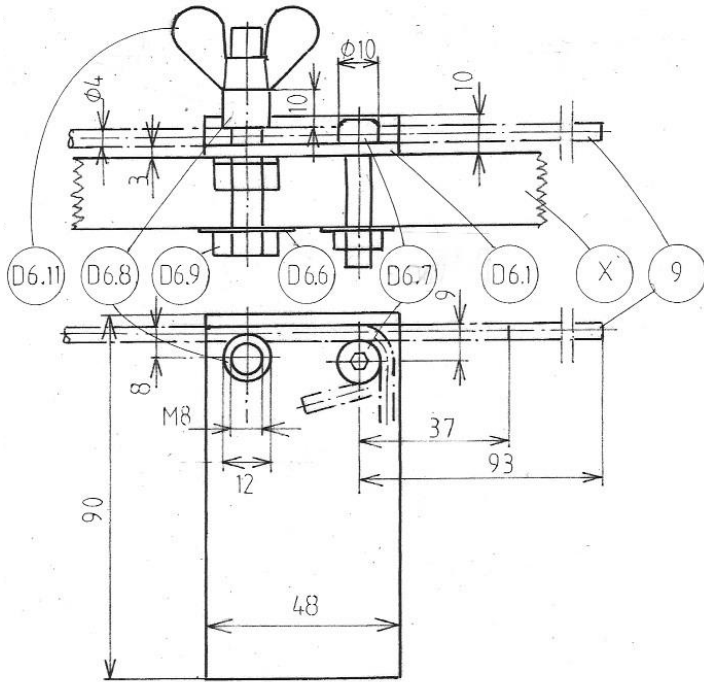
Dibujo del dispositivo D6 para doblar soporte del recipiente (6), de acero (soporte soldado), o de aluminio o acero inoxidable (soporte con abrazaderas); diámetro: 4 mm
